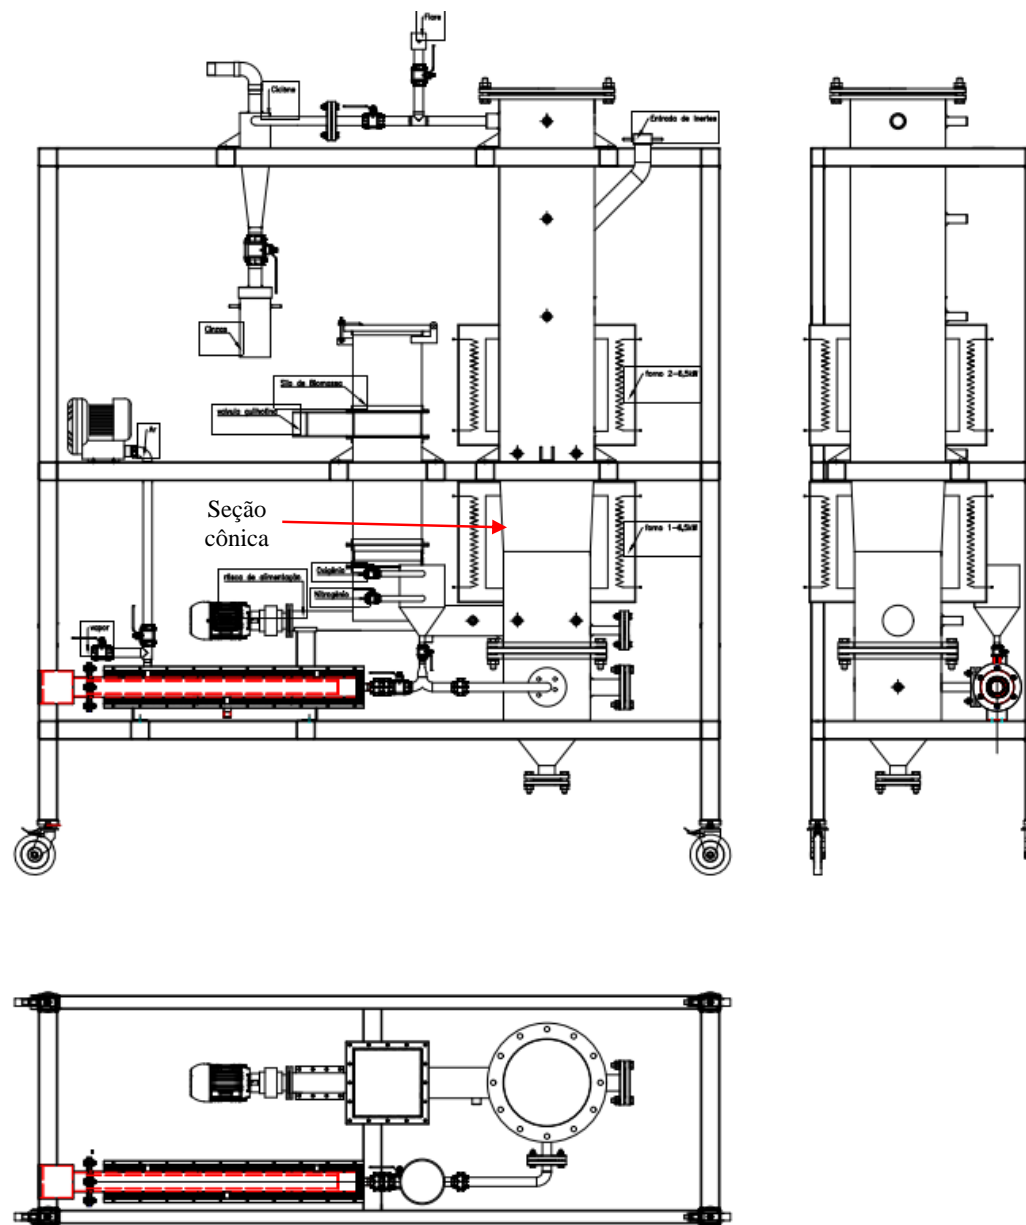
Desenho de Conjunto do Gaseificador Projetado e Construído
